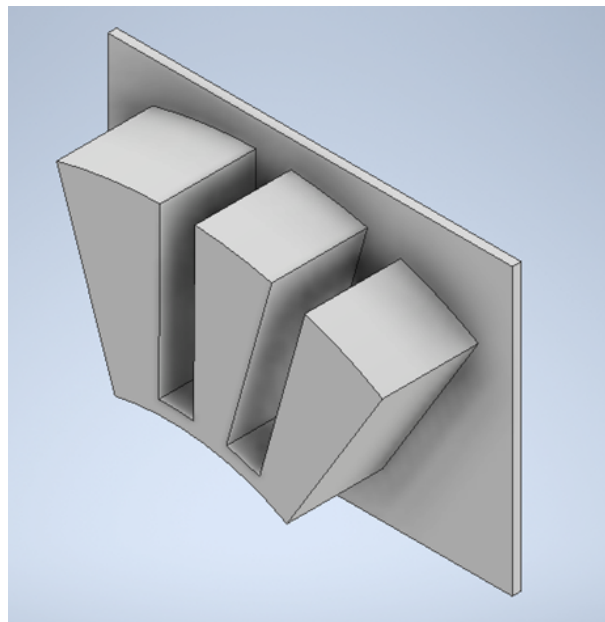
Diseño del molde en positivo del actuador blando. Elaborado por los autores.
